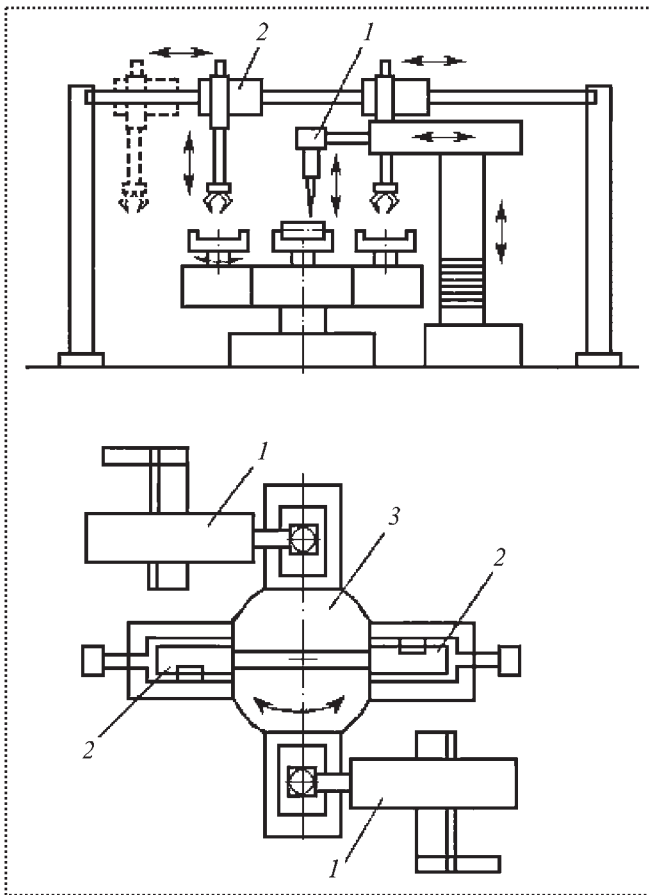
Роботизированный комплекс для электродуговой сварки сложных узлов
